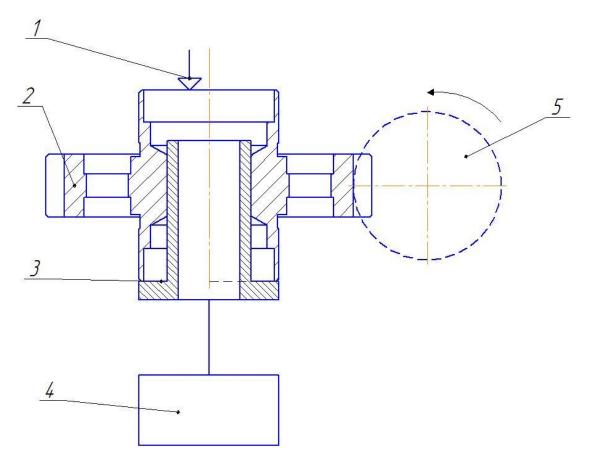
Принципиальная схема приспособления: 1 – установочные элементы; 2 – деталь; 3 – опорная втулка; 4 - корпус приспособления; 5 – фреза.
